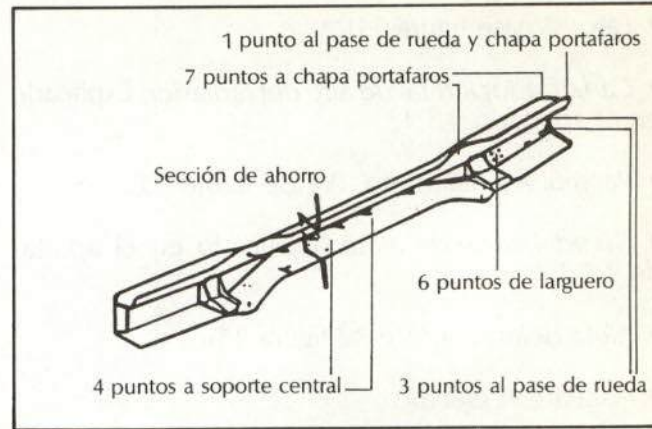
Unión de la traviesa inferior con carrocería. Sección de ahorro.
